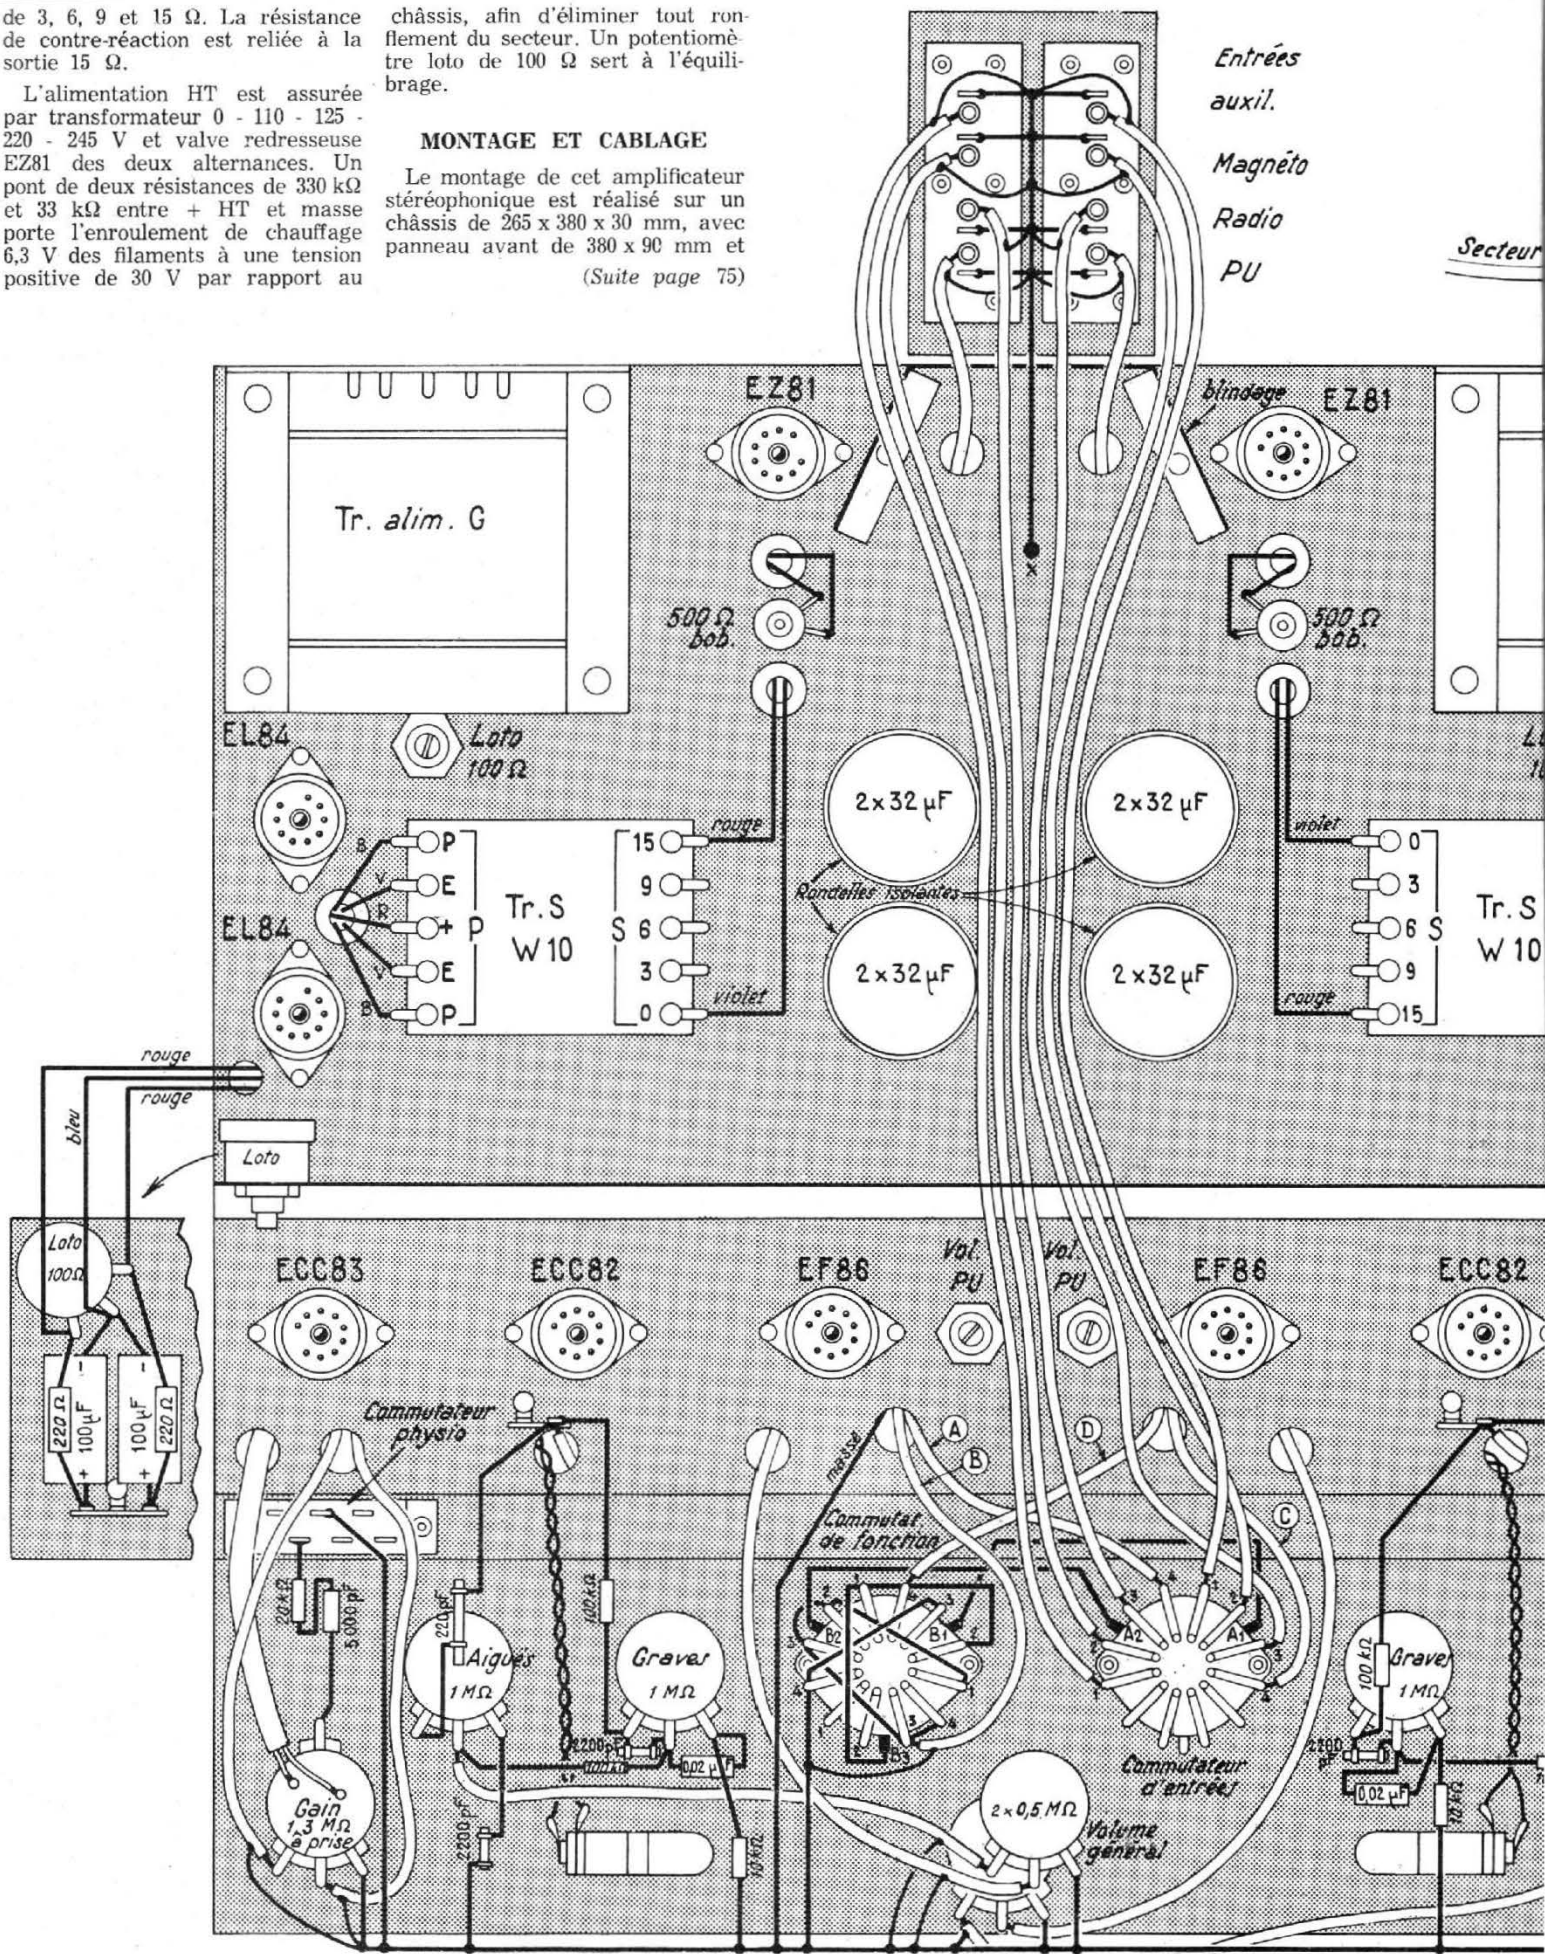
Vue de la partie supérieure du châssis ; les faces avant et arrière sont représentées rabattues
